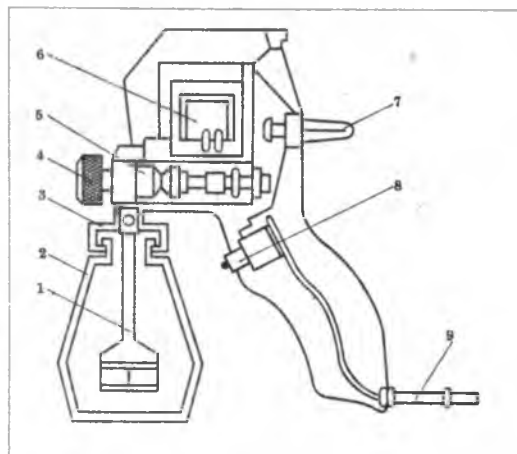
Схема электрического распылителя «Ореол-5М4»: 1 — всасывающая трубка с фильтром; 2 — бачок; 3 — корпус; 4 — сопло; 5 — насос; 6 — дроссель; 7 — ручка регулирования подачи краски; 8 — кнопка выключения насоса; 9 — соединительный шнур
